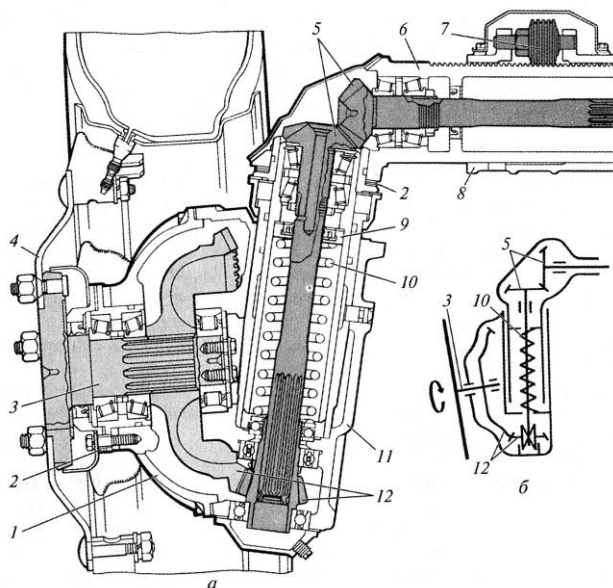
Колісний редуктор переднього ведучого моста трактора МТЗ-82: а – будова; б – схема; 1 – кришка корпусу; 2 – регулювальні прокладки; 3 – ведений вал; 4 – диск колеса; 5, 12 – верхня і нижня пари конічних шестерень; 6 – висувний корпус; 7 – черв'ячний механізм; 8 – корпус ведучого моста; 9 – опора пружини; 10 – пружинна ресора; 11 – корпус редуктора
